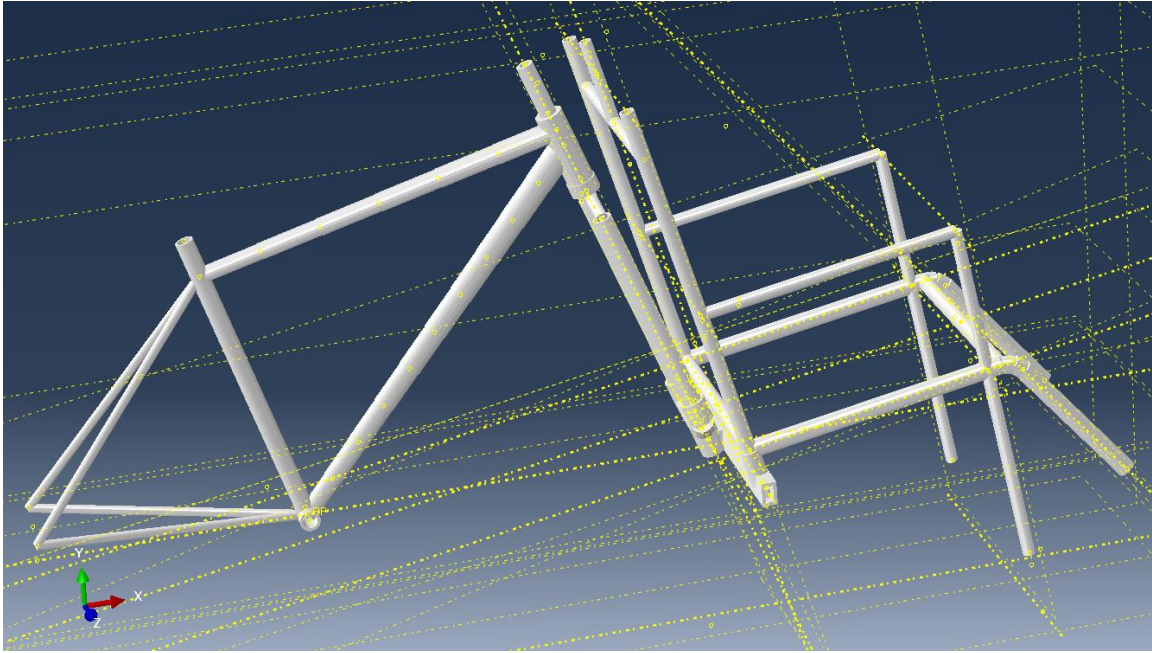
Nuevo diseño tras incorporar el resto de los elementos estructurales (Vista 2).
